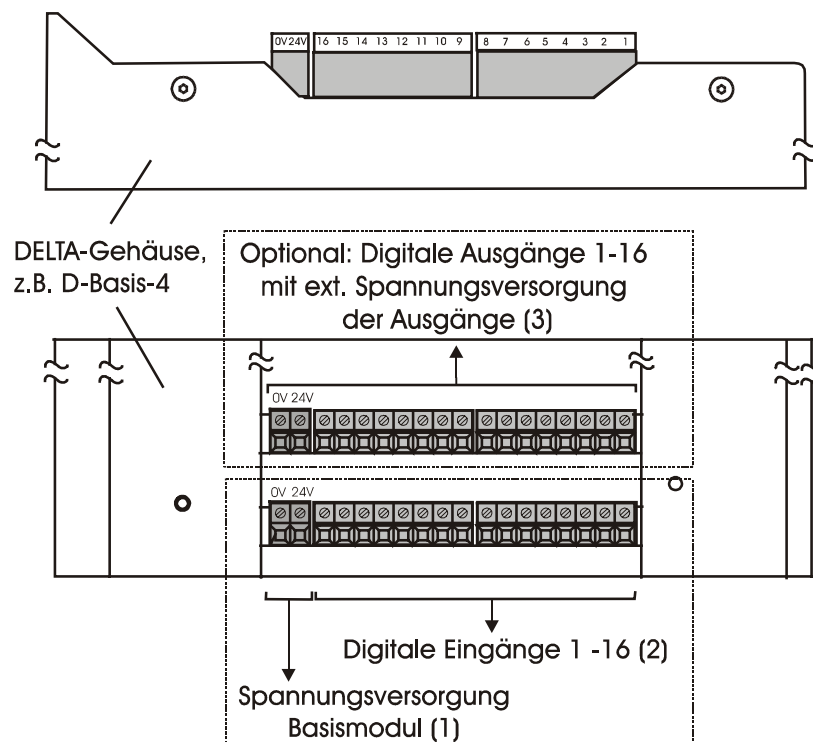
Draufsicht und Seitenansicht DELTA-Basisgehäuse
